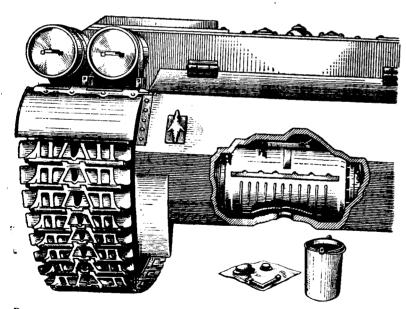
Отверстия для слива масла из картера механизма передач и поворотов
